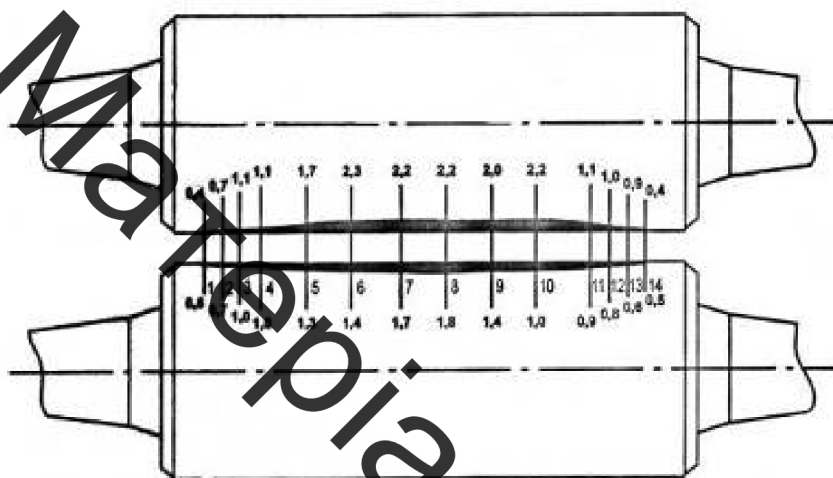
Зношення (мм) робочої поверхні валка
